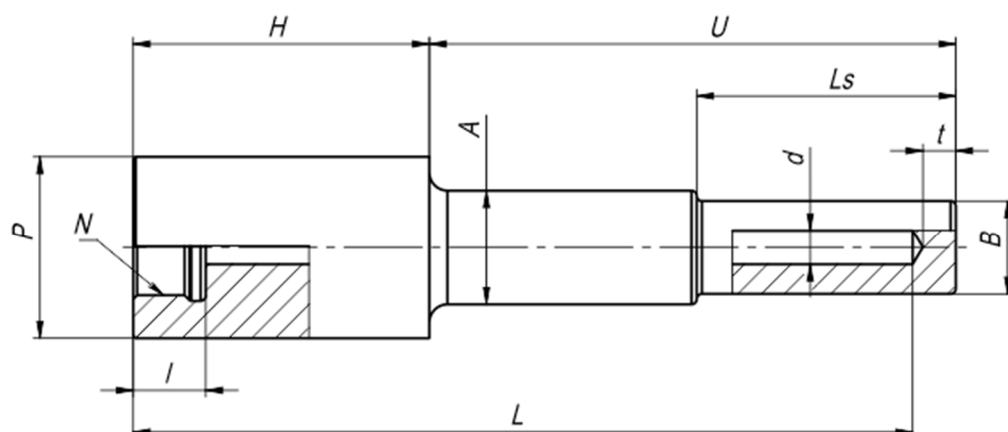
Гильза под приварку через адаптер (Socket Weld), цельноточёная, ступенчатая, под неподвижный штучер.
